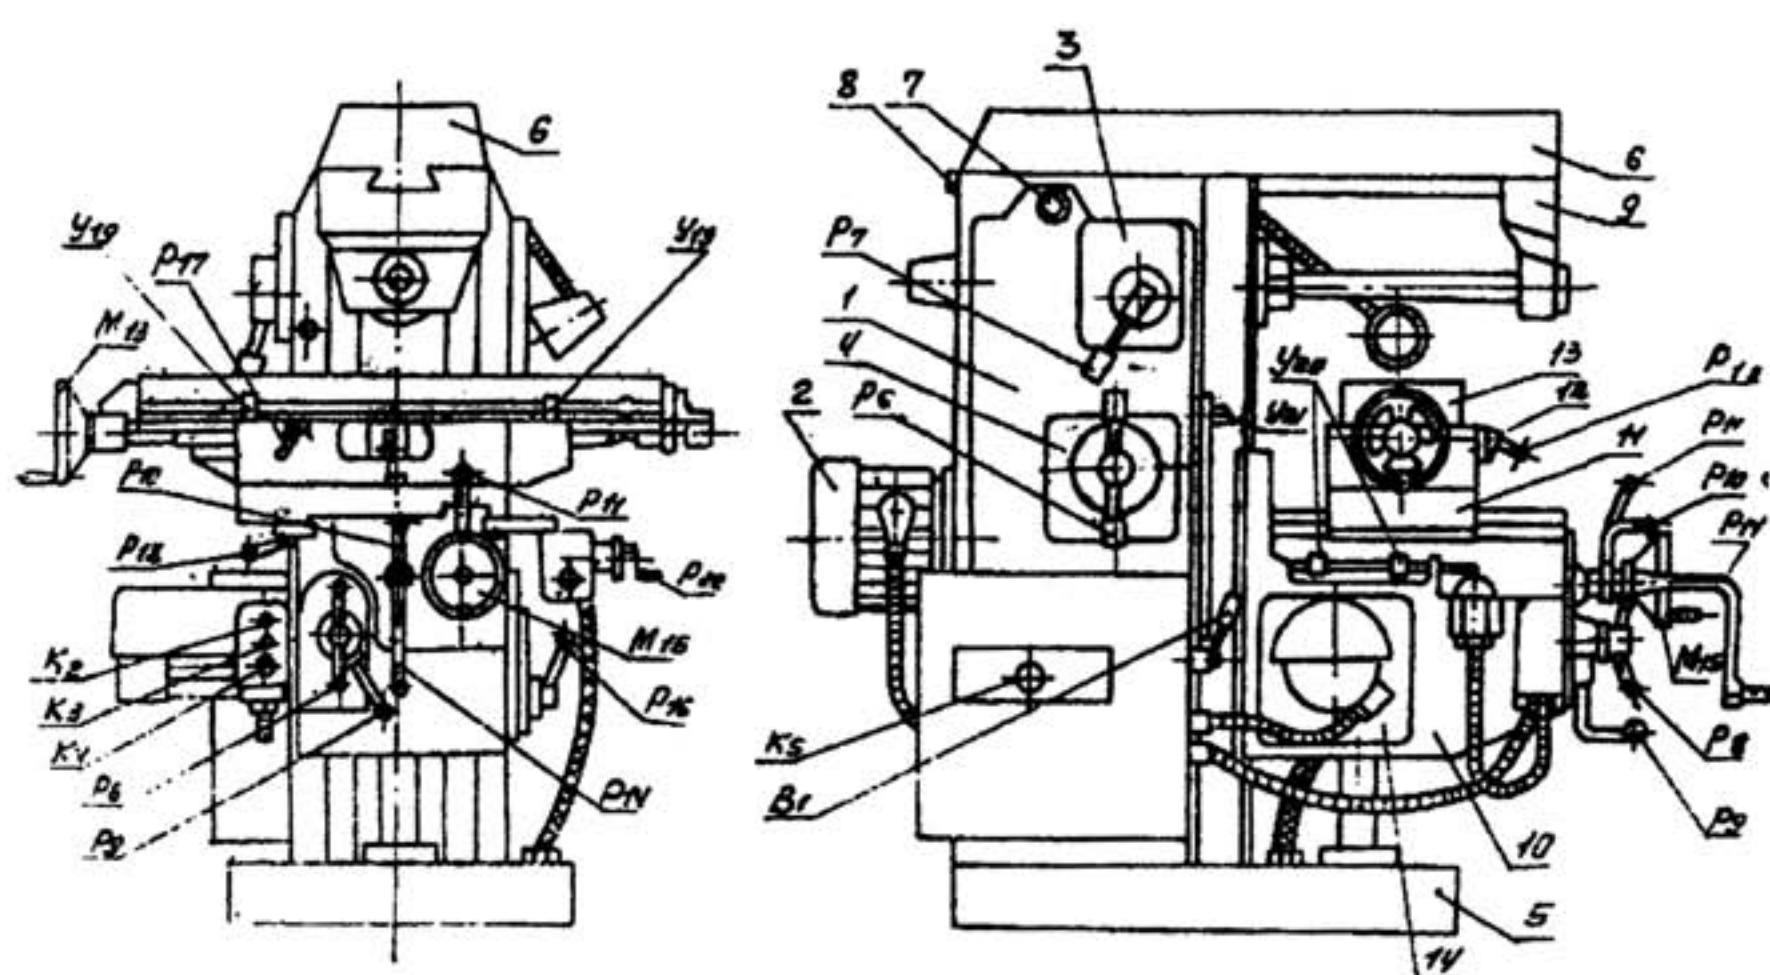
Горизонтально-фрезерный станок мод. 6Р81
